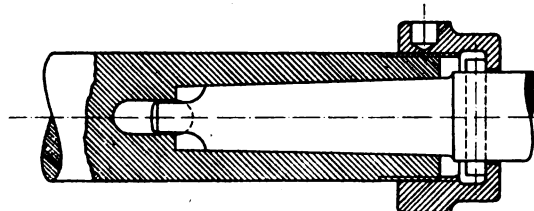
Werkzeugbefestigung mit Ueberwurfmutter.
